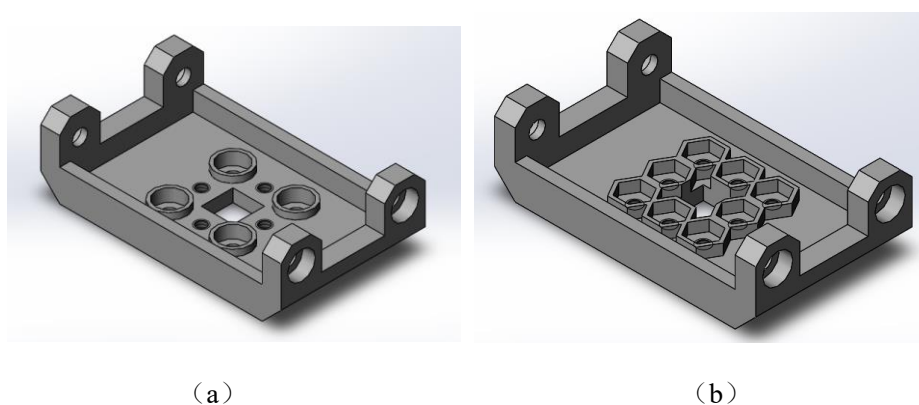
关节 2 零件图 (a) 有装螺丝的结构 (b) 有装螺母的结构
